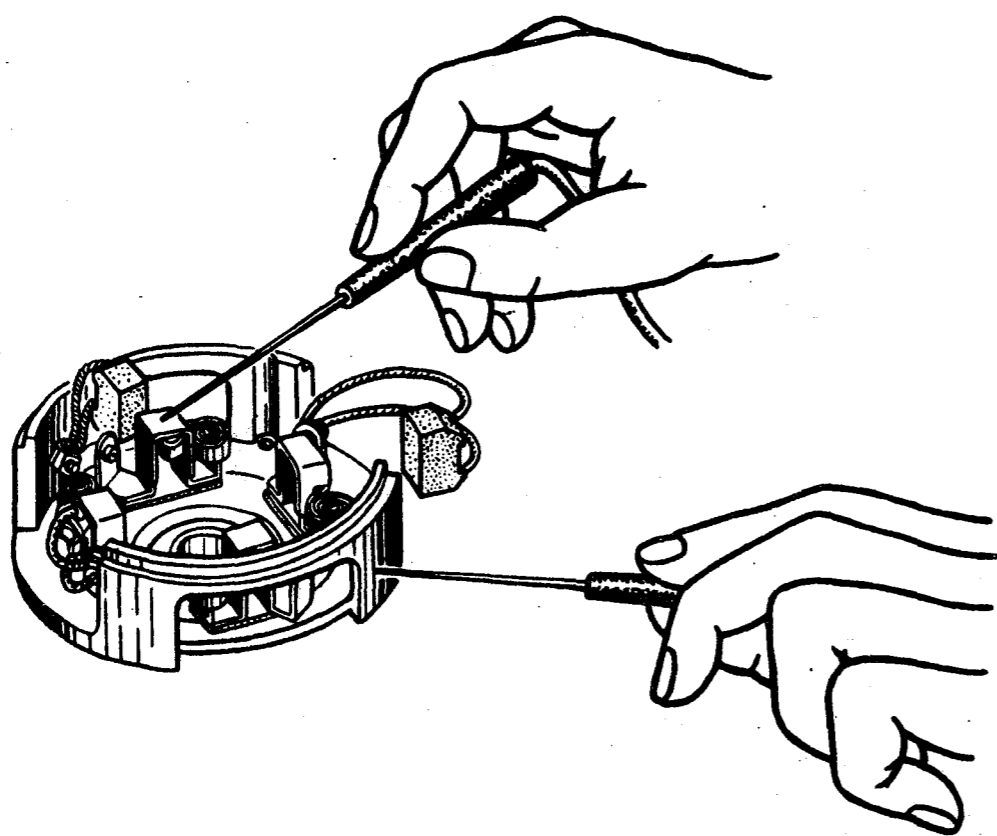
Проверка изолированных щеткодержателей стартера на замыкание с корпусом
